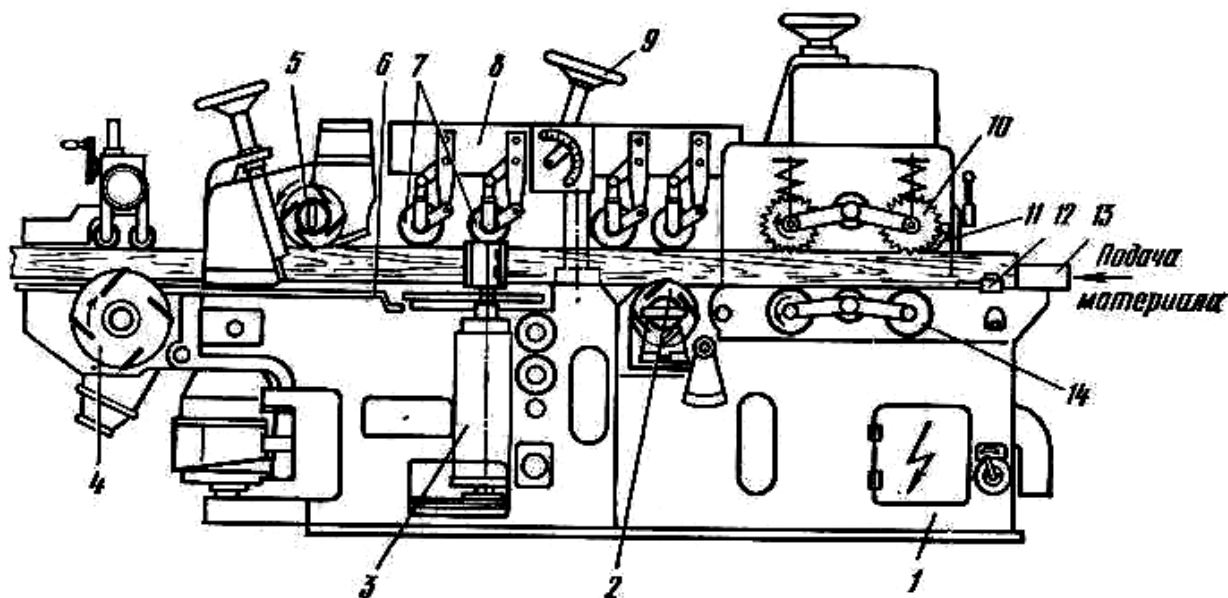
Четырехсторонний продольно-фрезерный станок С26 2М: 1 — станина, 2 — нижний шпиндель, 3 — левый шпиндель, 4 — калевочный суппорт, 5 — верхний шпиндель, 6 — стол, 7 — прижимные ролики, 8 — суппорт прижима, 9 — маховички, 10, 14 — вальцы, 11 — когтевая защита, 12 — боковой прижим, 13 — направляющая линейка
